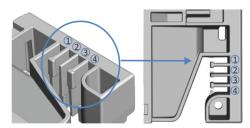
Schlauchkanal mit Schlauchführungen (links: Ansicht von innen, rechts: von oben)
